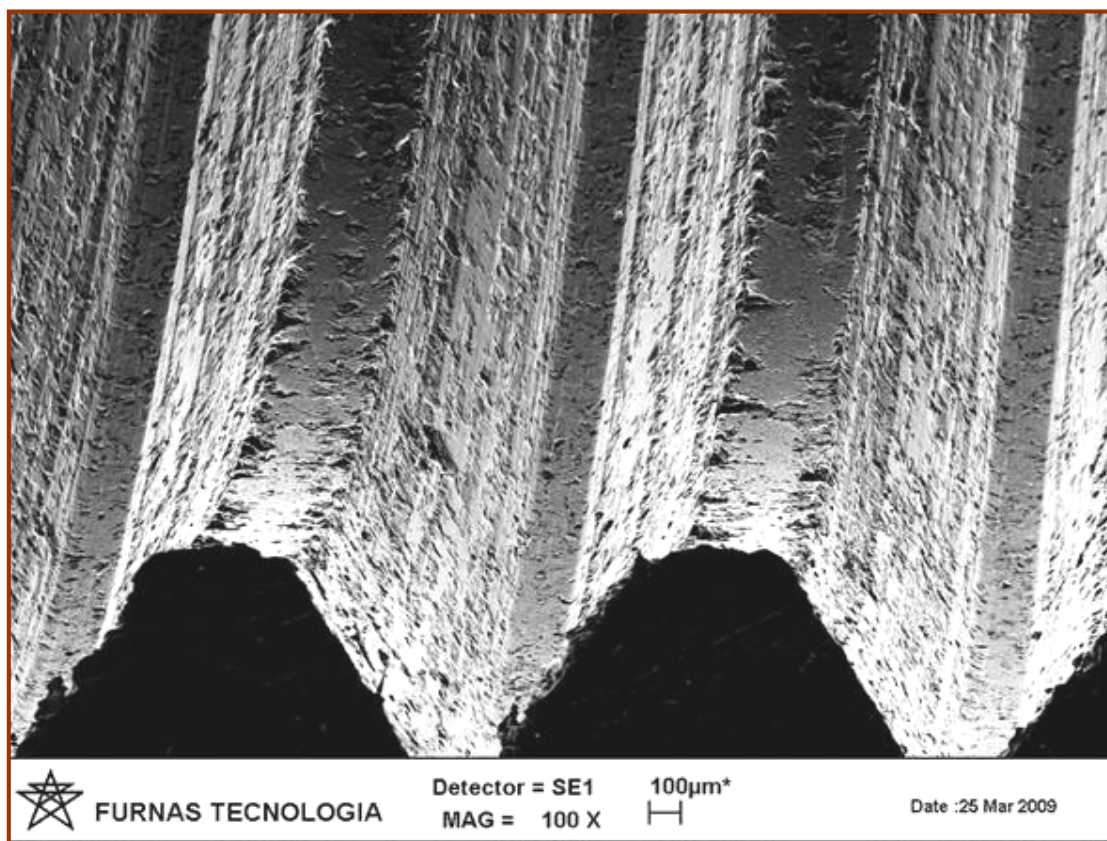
Imagem de uma rosca usinada em ferro fundido vermicular (50 m/min) com macho de corte de metal duro (fim de vida – após usinar 12000 roscas) com fluido de corte em forma de jorro (região intermediária da rosca)
